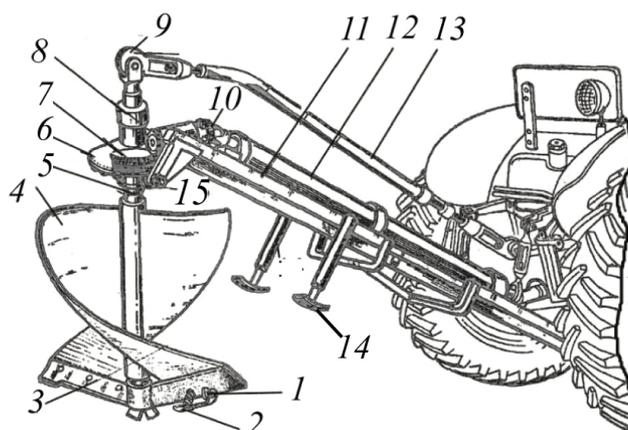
Копатель ям универсальный КЯУ-100: 1 – регулировочный болт; 2 – опорная пятка; 3 – лемех; 4 – шнек бура; 5 – вертикальный вал; 6 – корпус редуктора; 7, 8 – большая и малая конические шестерни; 9 – верхний шарнир; 10 – карданная передача; 11 – брусья рамы; 12 – кожух; 13 – верхняя тяга; 14 – выдвижные пятки; 15 – нижний шарнир
